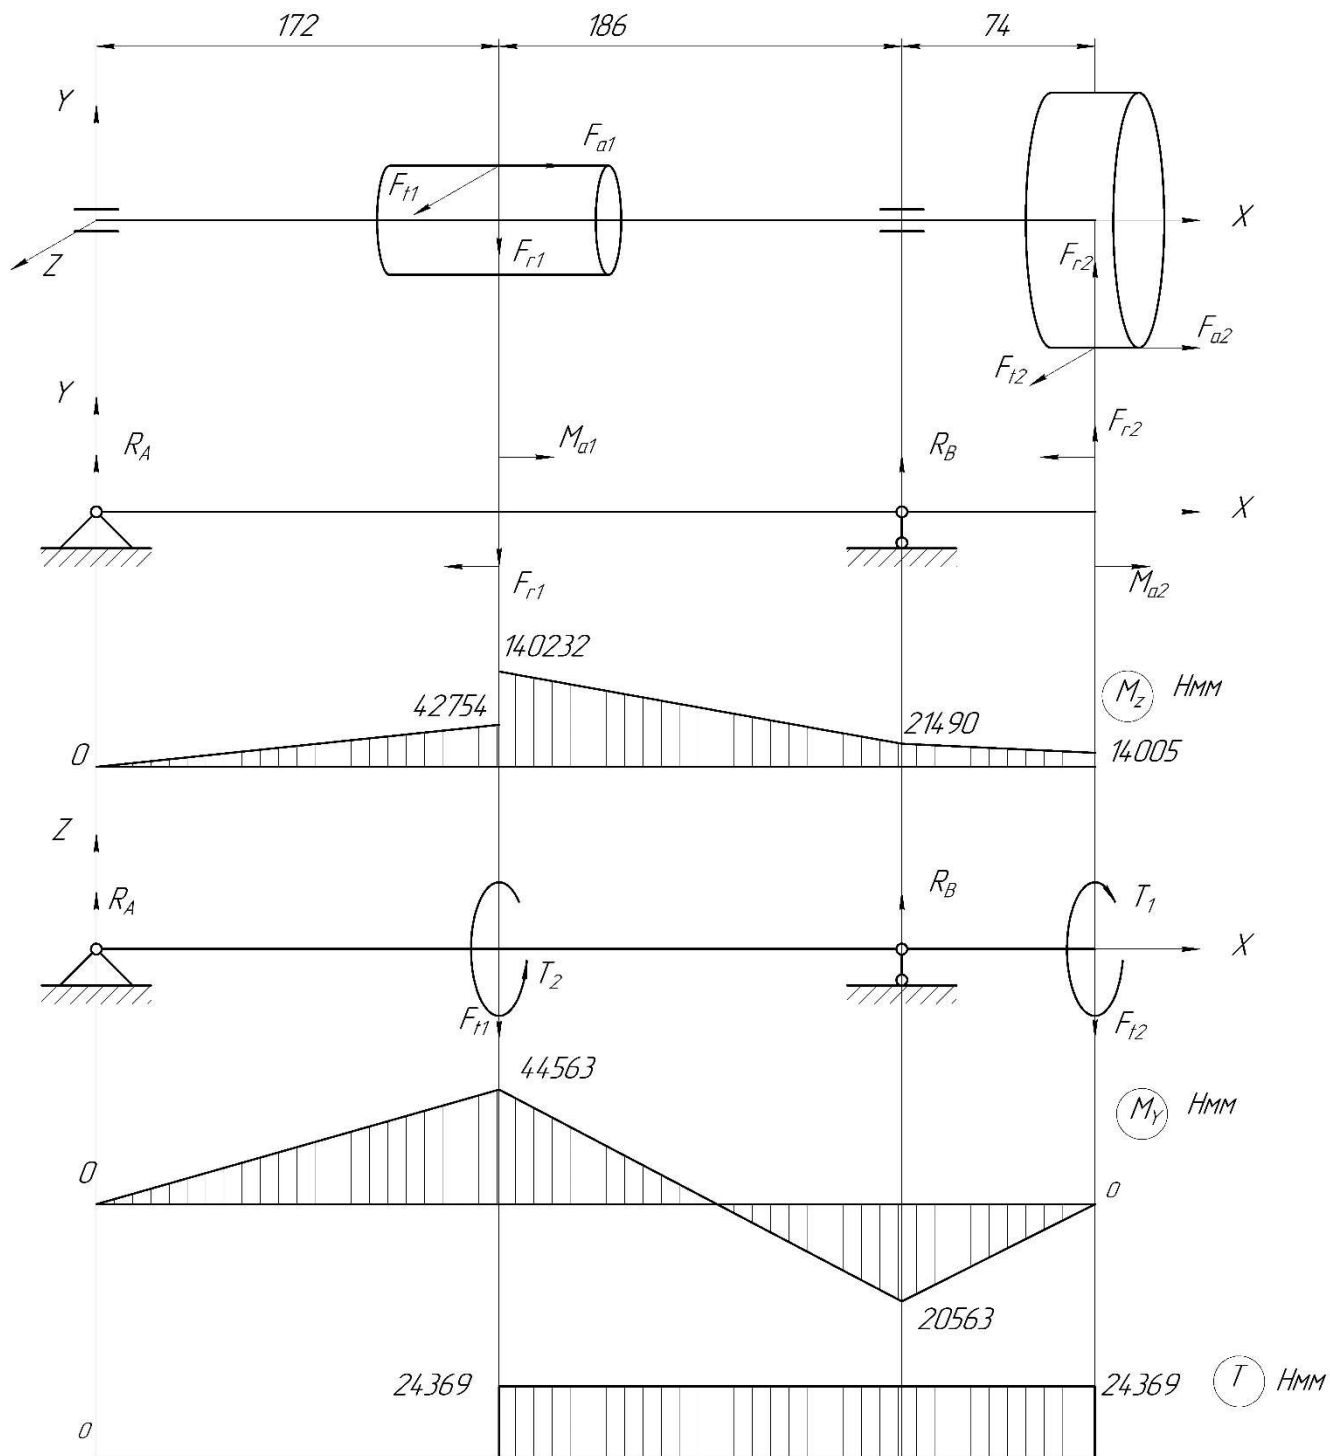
Розрахункові схеми проміжного вала редуктора
